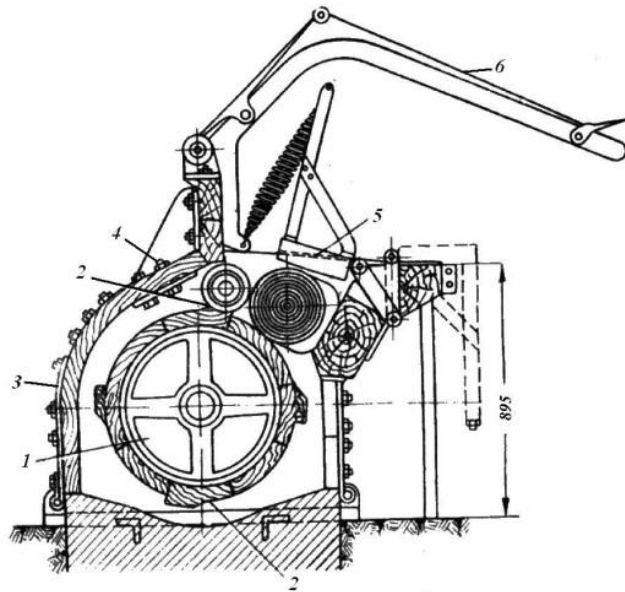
Кулачкова машина В'язового: 1 – барабан; 2 – ребро; 3 – кожух; 4 – кришка; 5 – валик; 6 – рукоятка.
